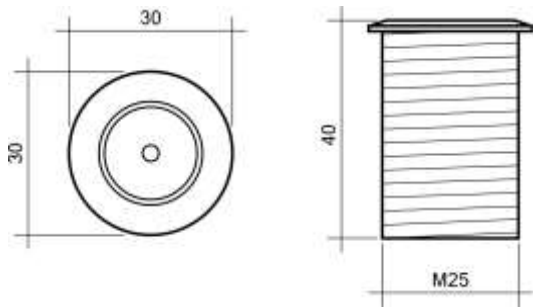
Считыватель QR-X-2 (врезной). Габариты изделия.
